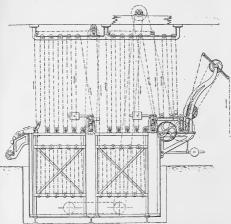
Gave continue à teindre en indigo; construction Welter.
